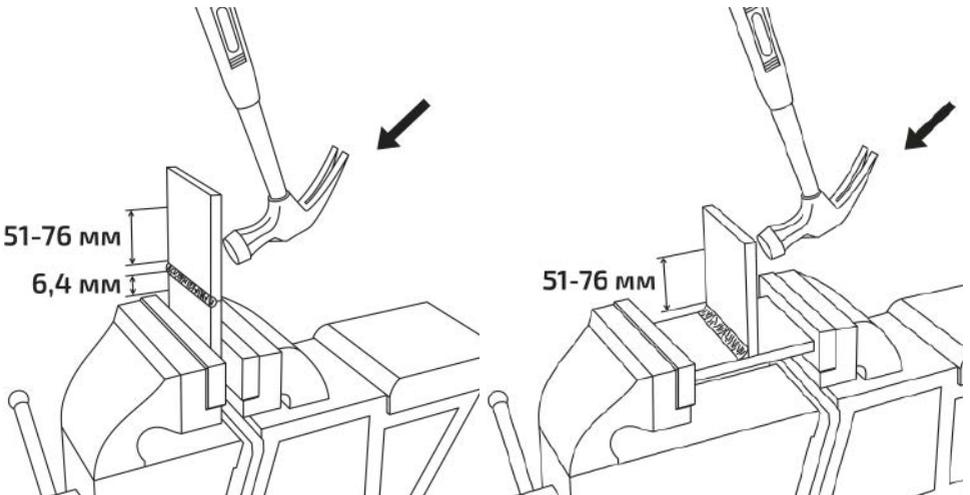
Проверка на прочность сварного соединения.
